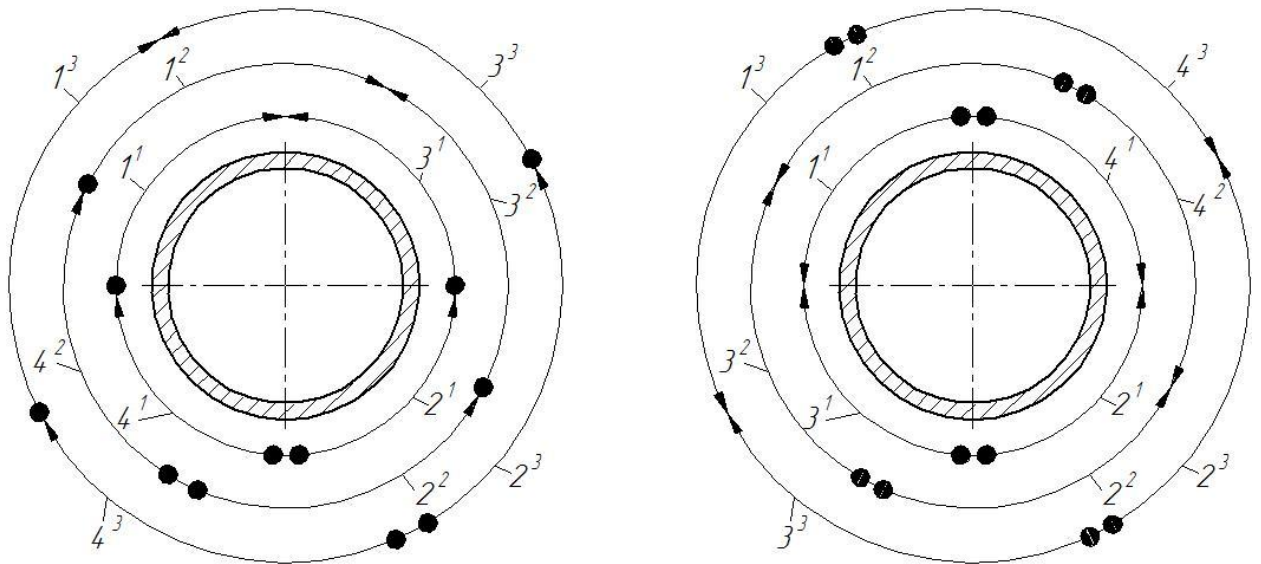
Порядок сварки слоёв при вертикальном (а) и горизонтальном (б) положении стыка
